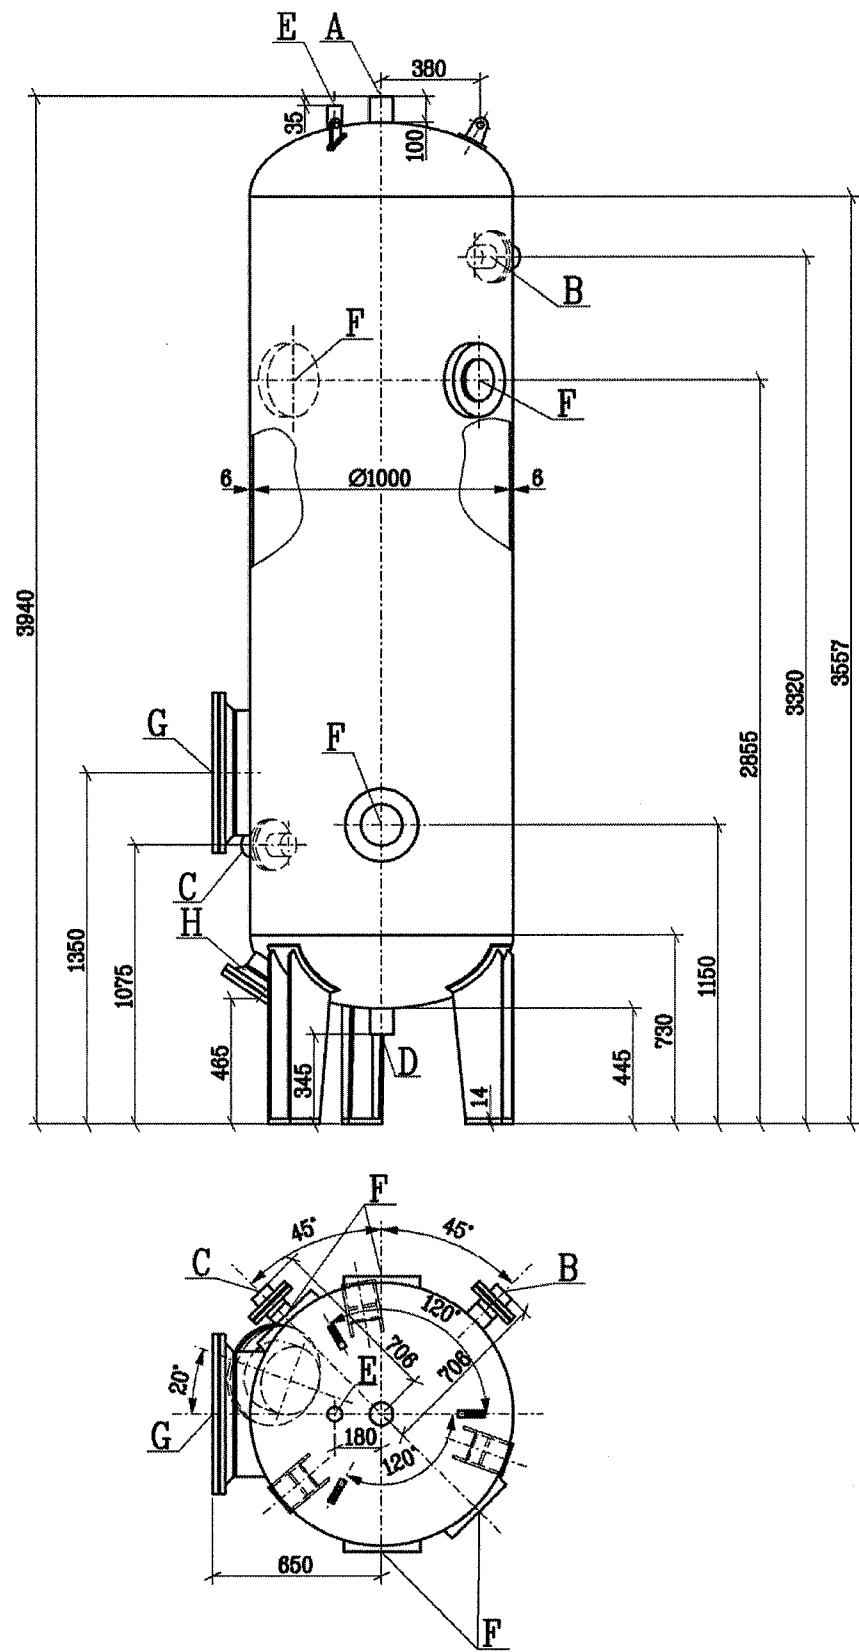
Габаритный чертеж фильтра сбора среднего слоя LDP44AT001
